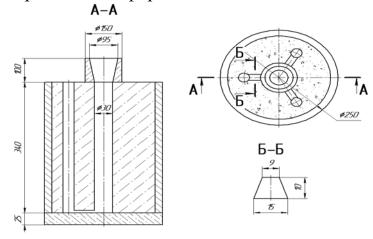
Форма для заливки образцов для механических испытаний
